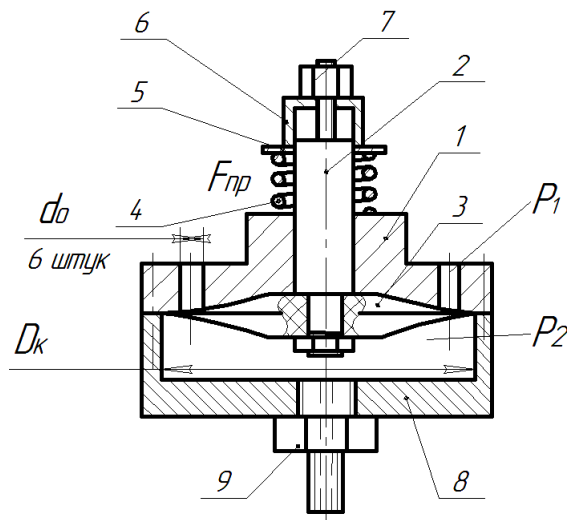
Розрахункова схема зворотного клапану вібраційної машини для очистки забруднень потоком пульсуючого струменя рідини з твердими частинками: 1 – корпус; 2 – шток; 3 – пружна мембрана; 4 – пружина; 5 – шайба; 6 – стакан; 7 – гайка регулювальна; 8 – кришка; 9 – штуцер
